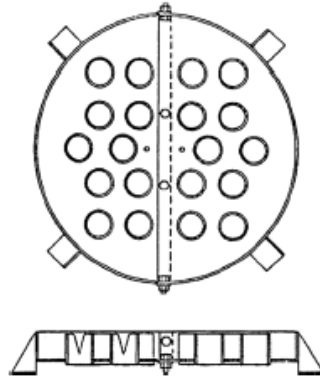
Distribuidor de tipo rebosadero. Fuente: [38]
